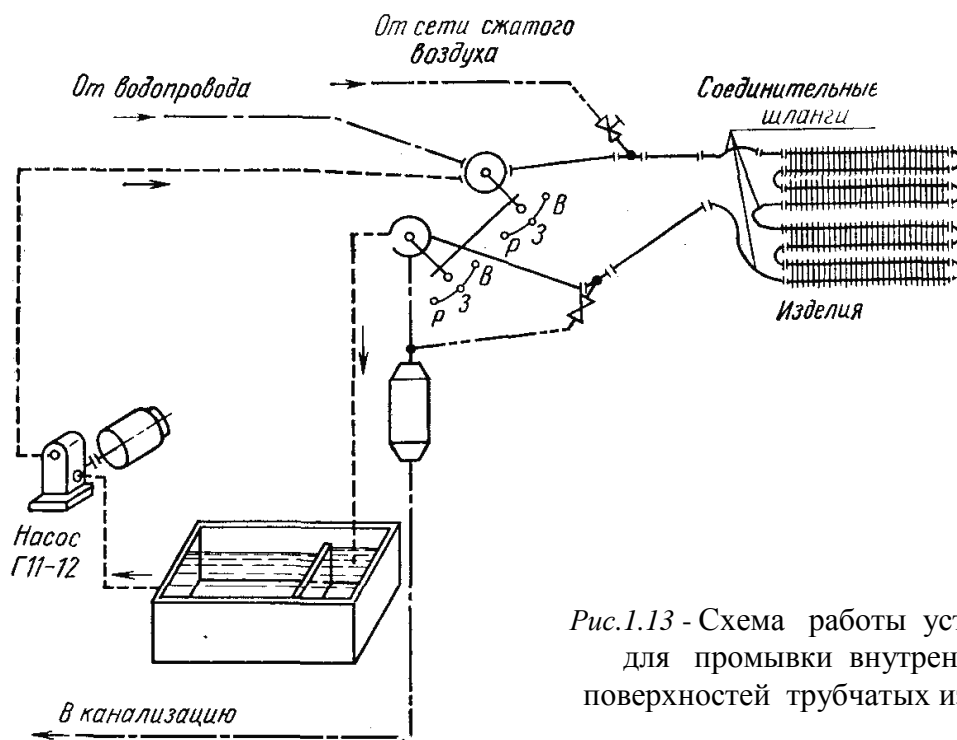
Схема работы установки для промывки внутренних поверхностей трубчатых изделий
